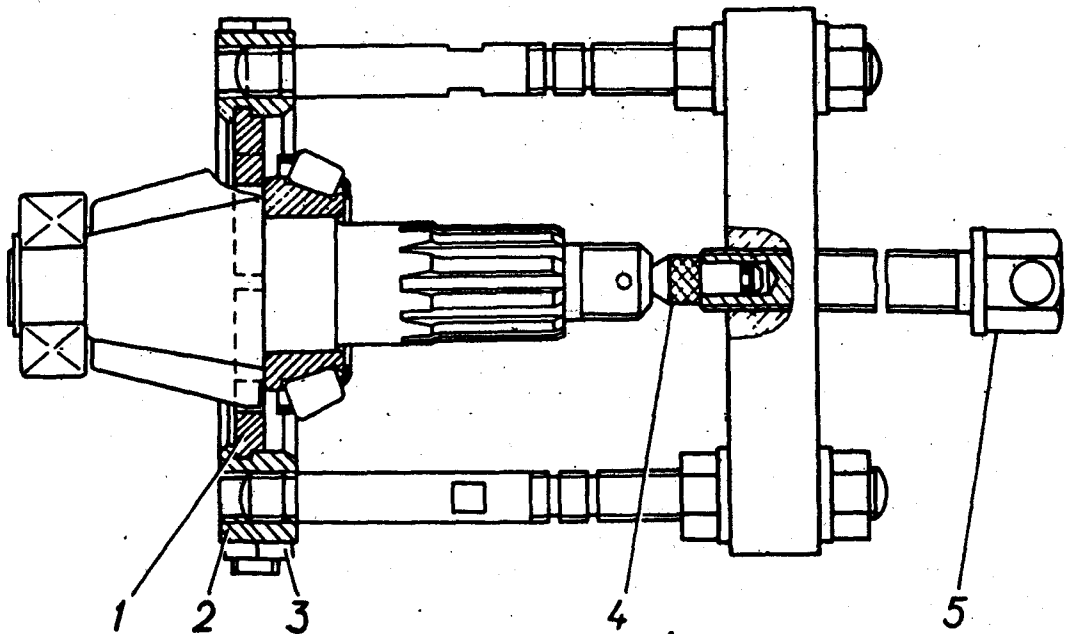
Выпрессовка внутреннего кольца заднего конического подшипника ведущей шестерни:
